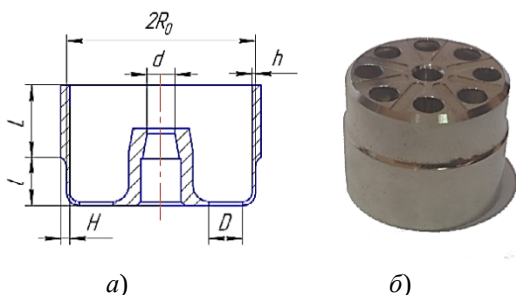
Схема циліндричного резонатора з циліндричним вузлом кріплення (а) та його загальний вигляд (б)
